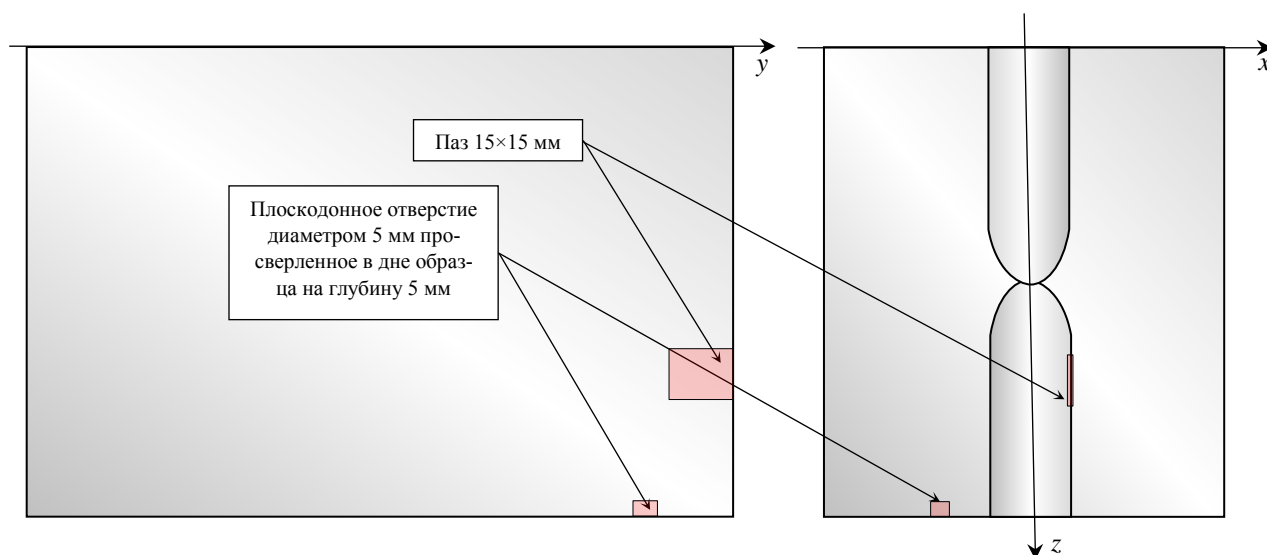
Схематическое изображение образца парогенератора с моделями отражателей
